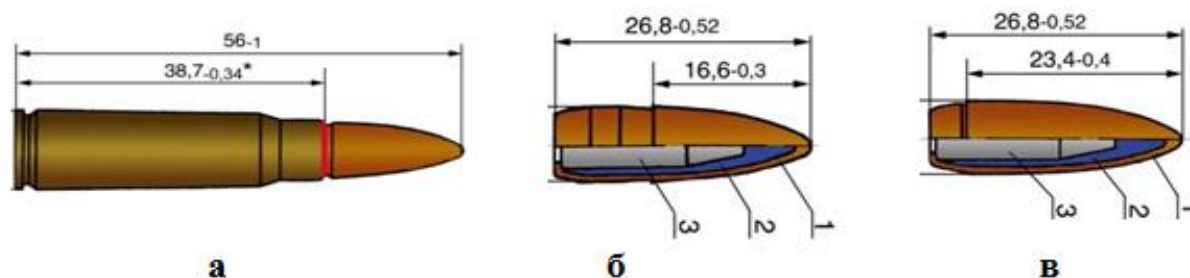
7,62x39-мм патрон обр. 1943 г. с пулей со стальным сердечником: а – патрон; б – пуля с канавкой; в – пуля с уступом; 1 – оболочка; 2 – рубашка; 3 – сердечник термоупрочненный из стали марки Ст. 70
